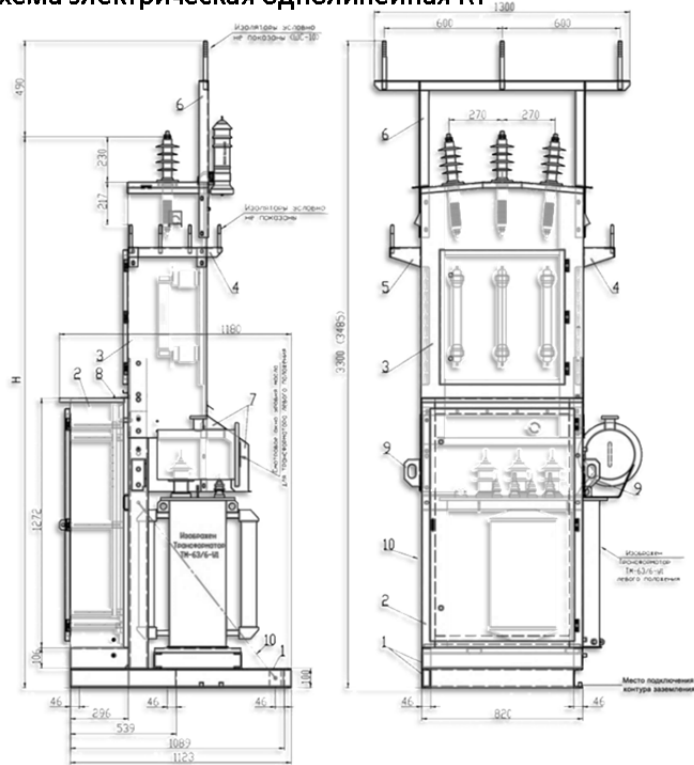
Внешний вид и габаритные размеры КТПН
